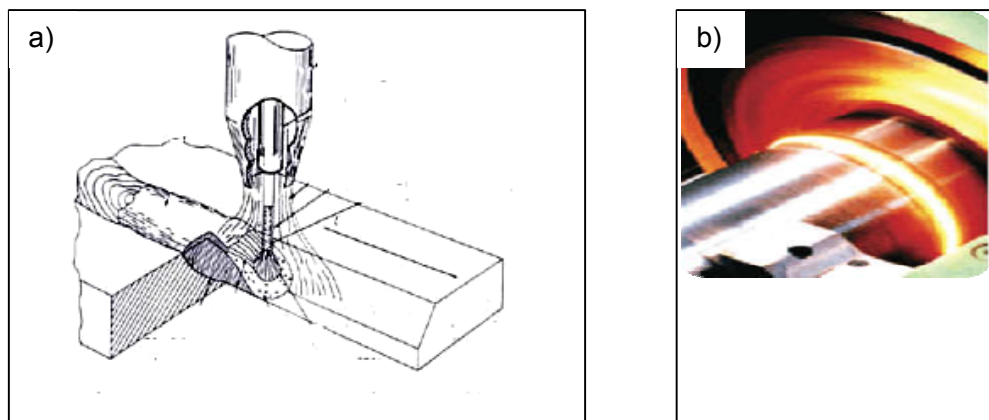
Proceso de soldadura para unión de metales. a) Unión por fusión por el proceso FCAW b) Unión en estado sólido por soldadura por fricción^[2].
